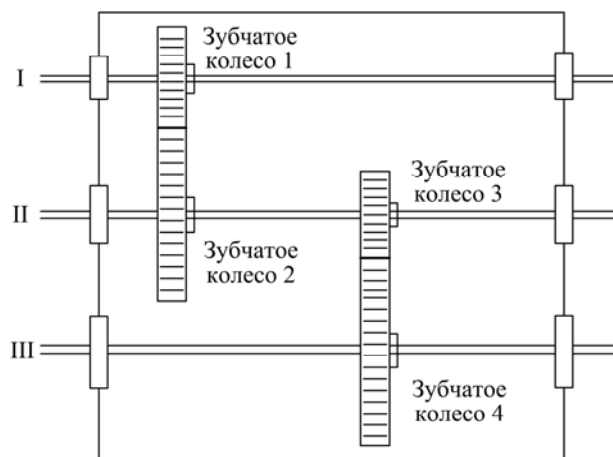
Схематическое изображение двухступенчатой зубчатой передачи
